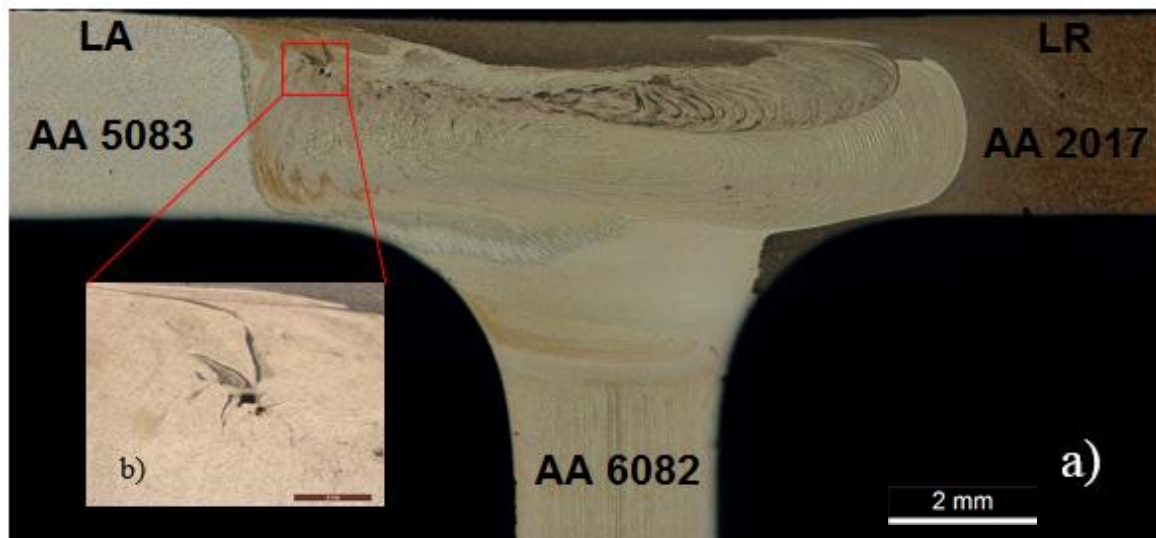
a) Macrografia da soldadura 562BRP-1e b) Ampliação do defeito (escala 2 mm)
